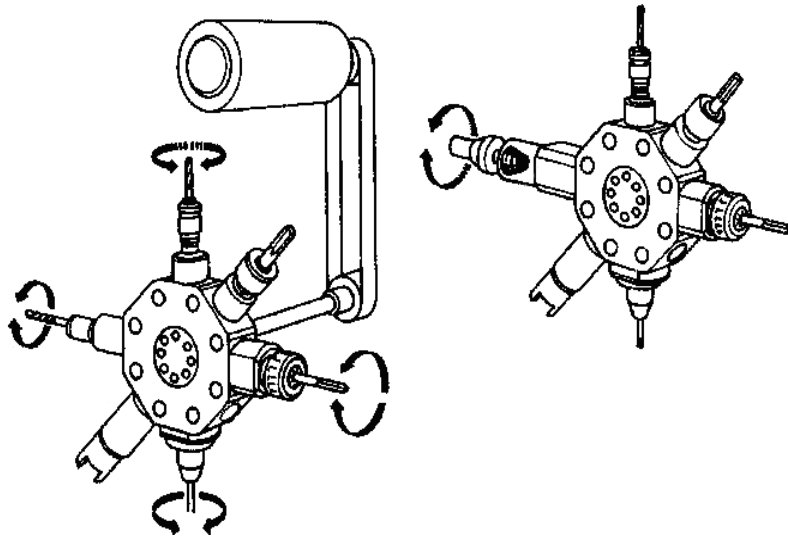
Конструктивная схема револьверной головки токарного станка с вращающимися шпинделями
